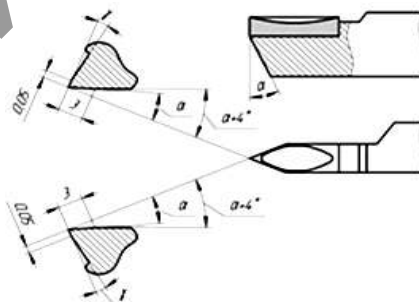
Резьбовой резец со сменной твердосплавной пластиной
